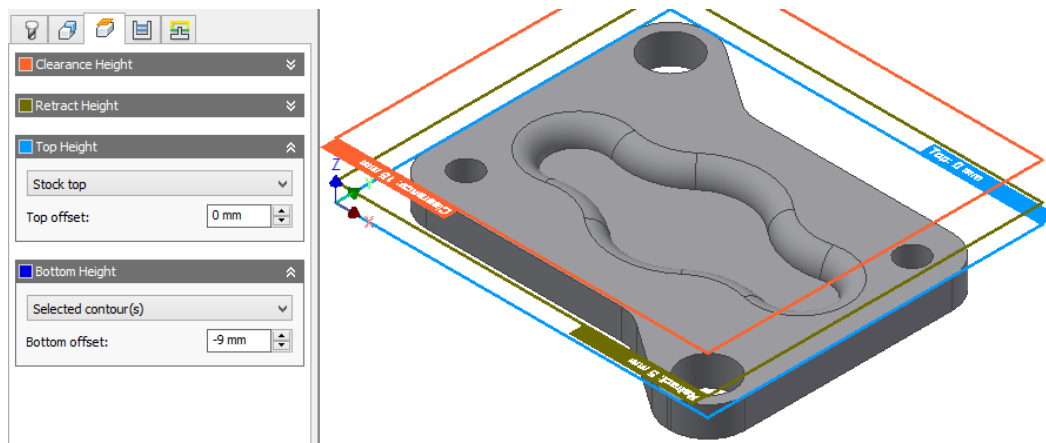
Wybrane rodzaje obróbki frezarskiej
